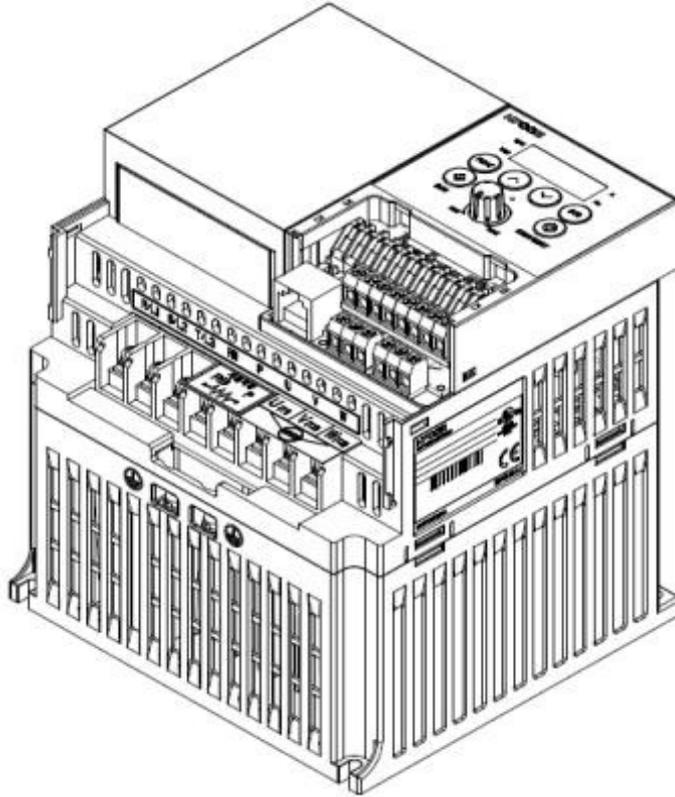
Способ открытия блока клемм инвертора N700E Inverter (3 конструкция)
